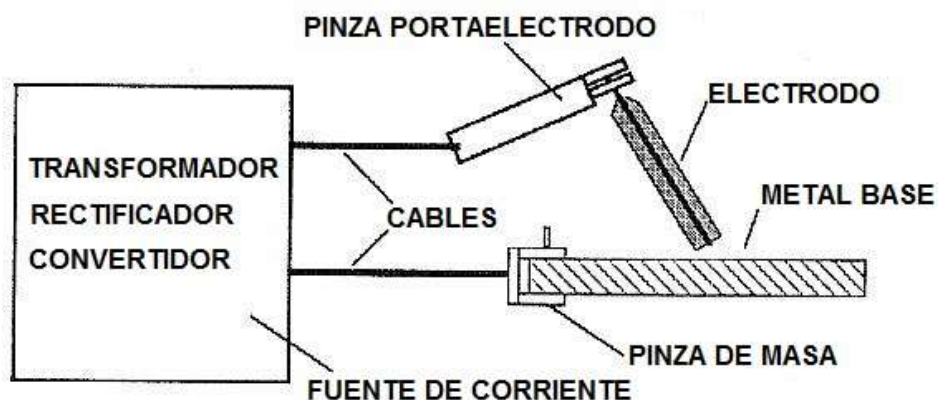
esquema de soldadura MMA, fuente: "Ingemecanica"
